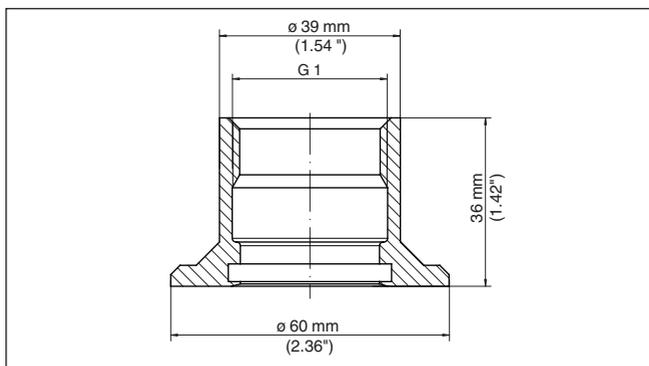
didas da luva para soldagem G1 (DIN 3852-A)
